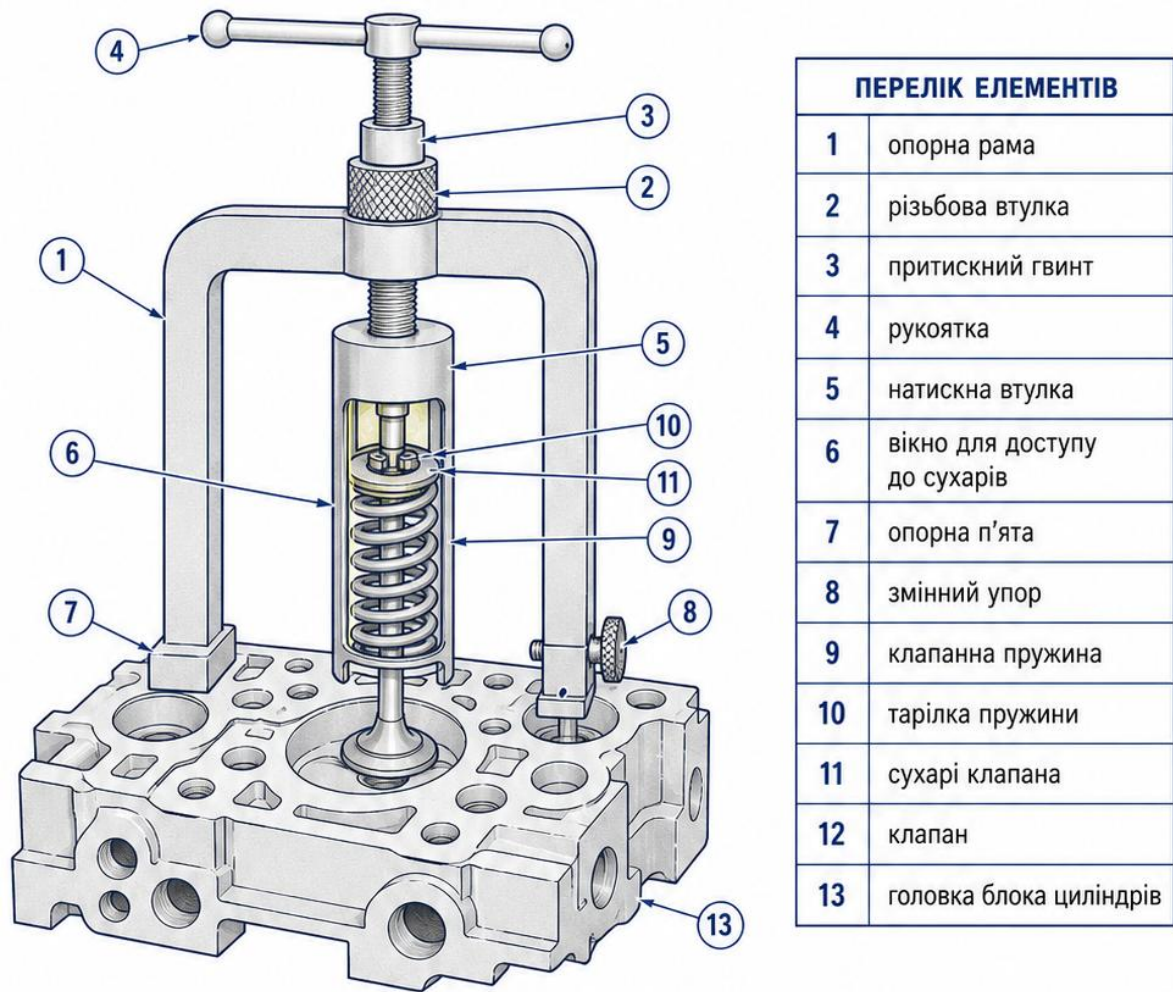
Схема пристосування для розсухарювання клапанів головки блока циліндрів.
